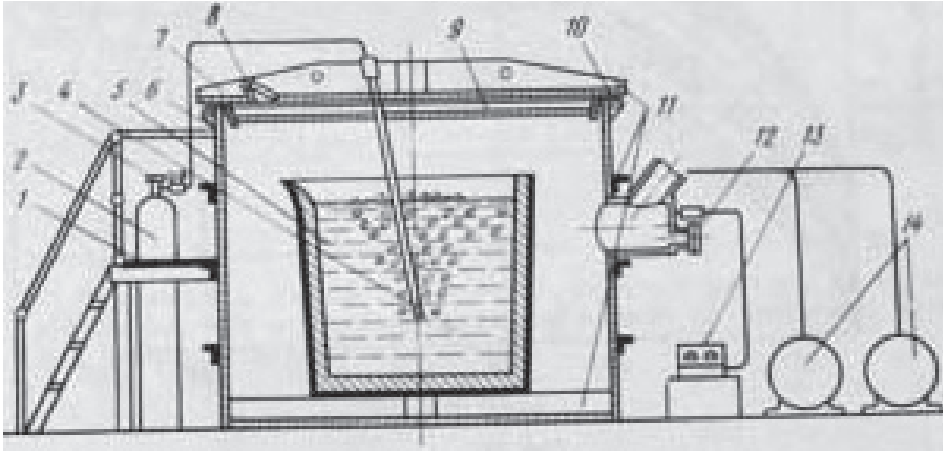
Схема установки для вакуумного рафинирования алюминиевых сплавов в ковше емкостью 3 т: 1 – площадка; 2 – баллон с аргоном; 3 – редуктор; 4 – газопровод; 5 – ковш; 6 – кожух камеры; 7 – крышка; 8 – смотровое окно; 9 – теплоизоляционный экран; 10 – уплотнение; 11 – ребра жесткости; 12 – патрубок; 13 – вакуумметр; 14 – насосы
